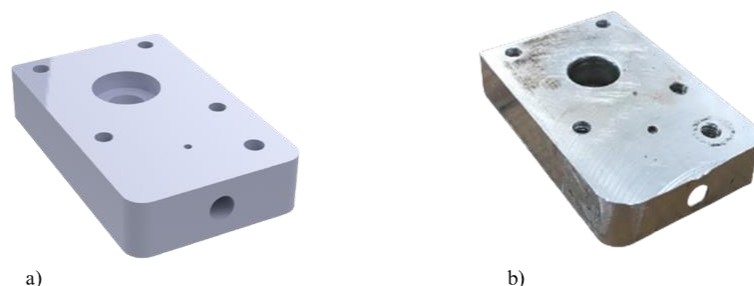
Base do *Shoulder*. a) Modelo em CAD 3D, b) Componente fabricado
